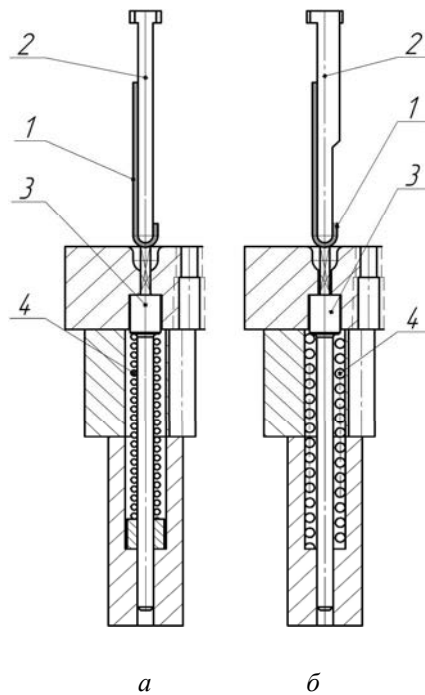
Механізм виштовхування деталі: 1 – виріб “Гачок”;
